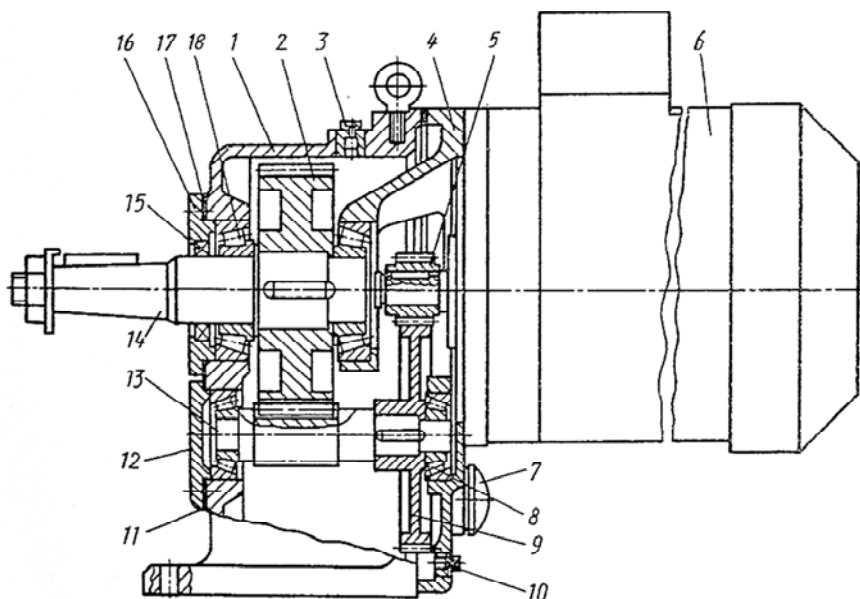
Цилиндрический двухступенчатый соосный мотор-редуктор
